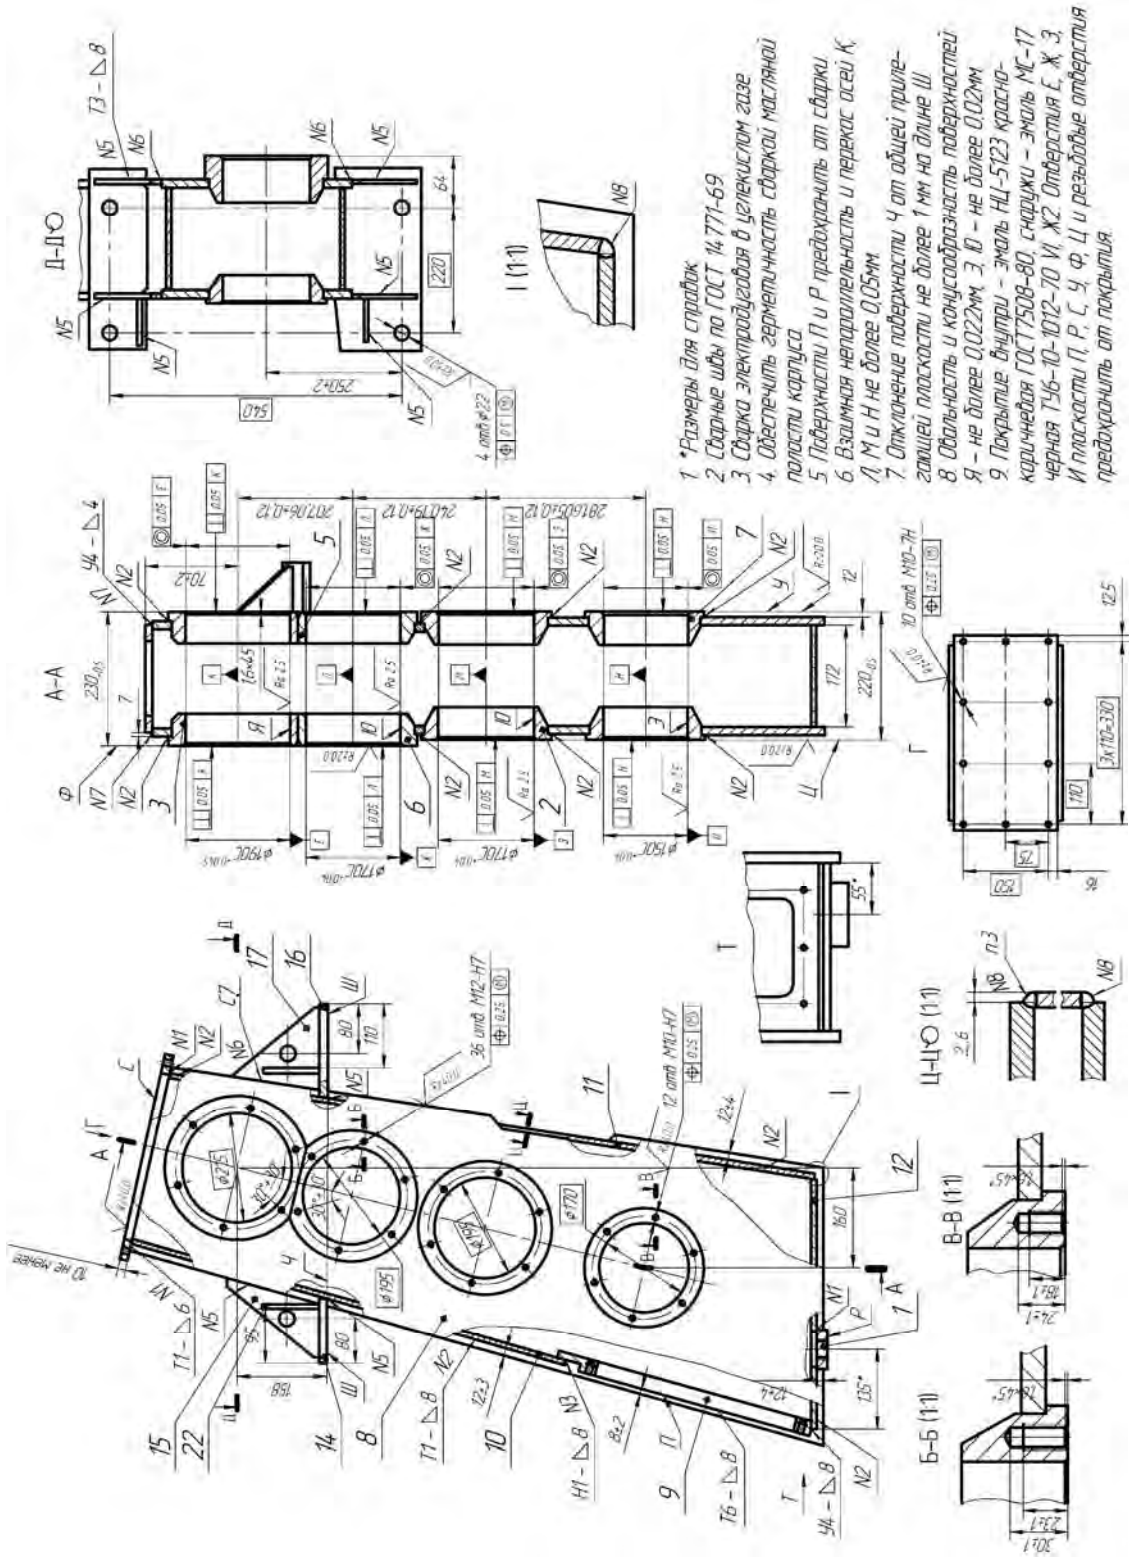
Чертеж корпуса промежуточного редуктора
